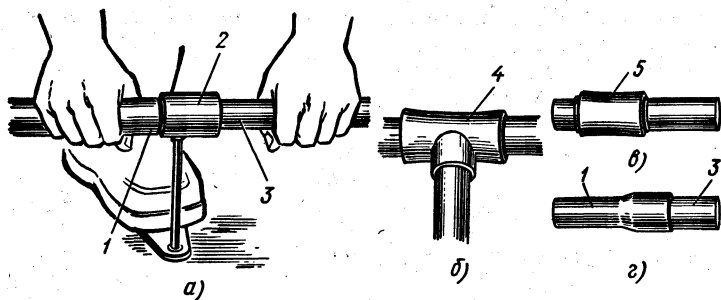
Контактная раструбная сварка (а) в литой тройник (б), муфту (в), раструб (г):
